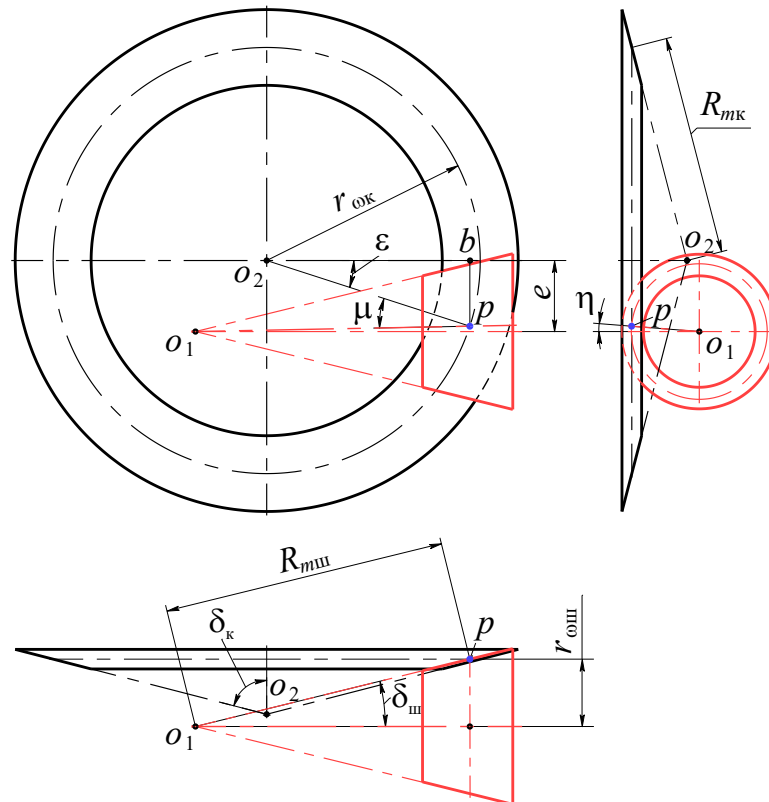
Схема розташування початкових конусів шестерні та колеса гіпоїдної передачі
